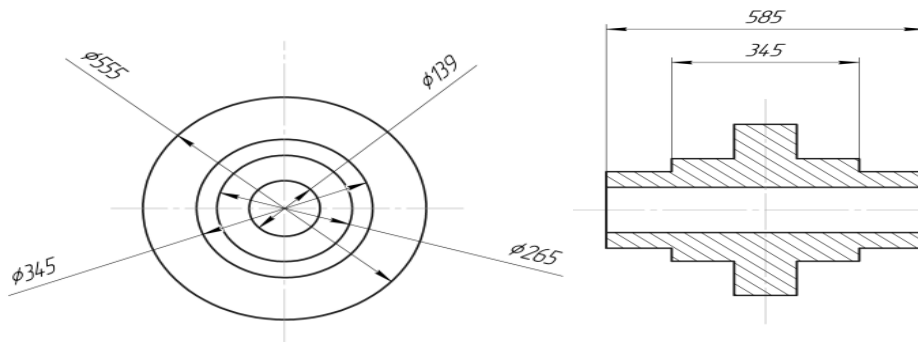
Эскиз детали «Заготовка червячного колеса»
